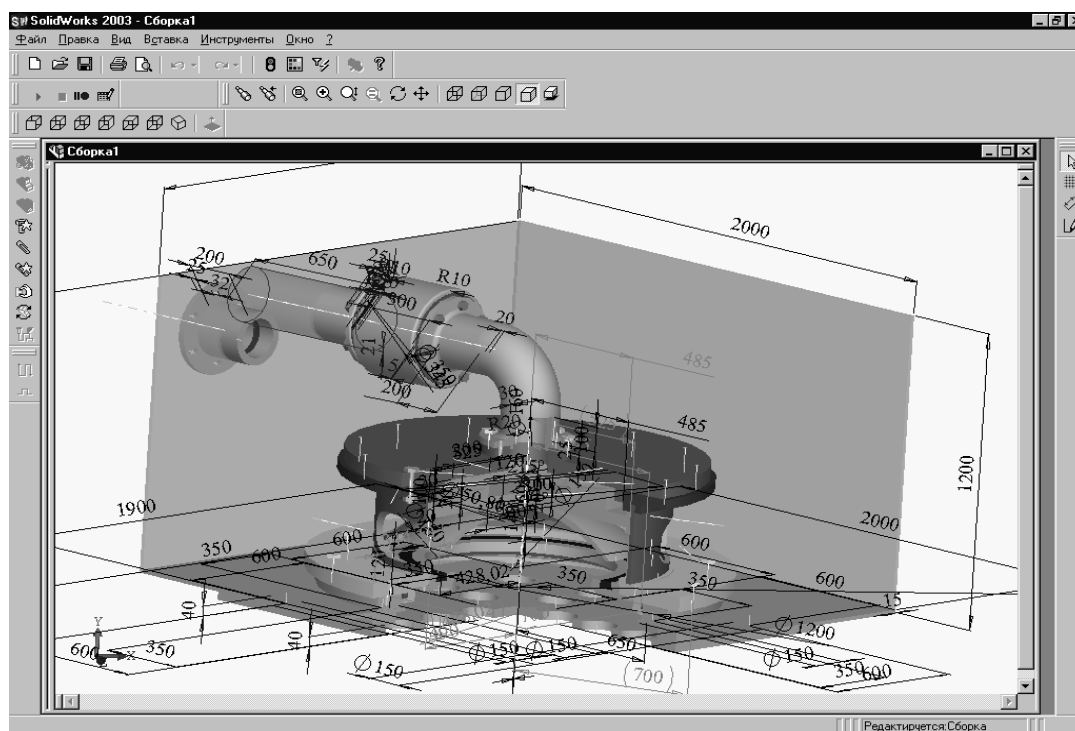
Сборочный чертеж импульсной головки низкого давления
